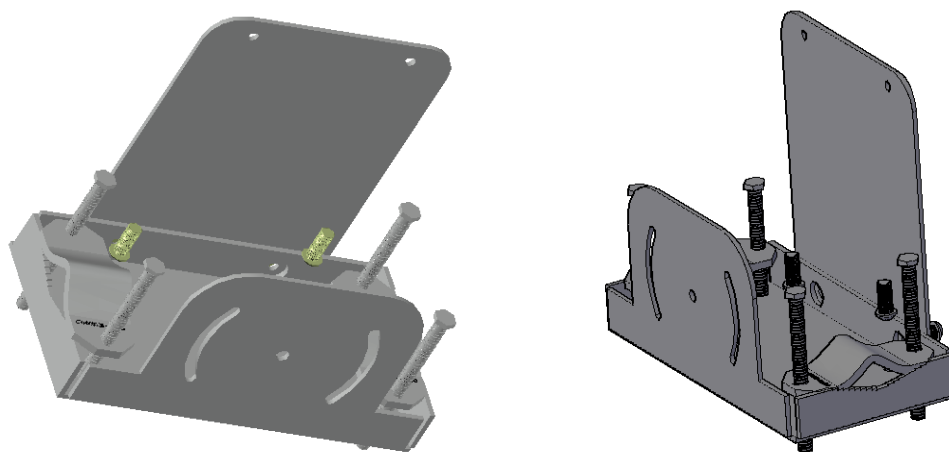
Kit de Montagem AP/Relay – Visões 3D
